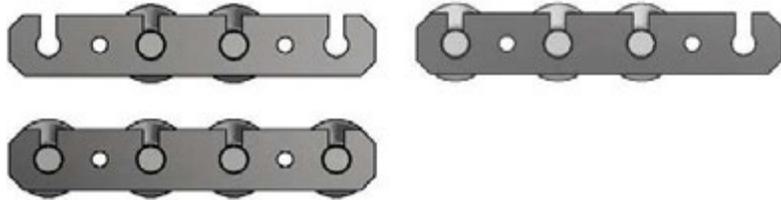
Plan de disposition pour les barrières ACCESSPARK-3500
